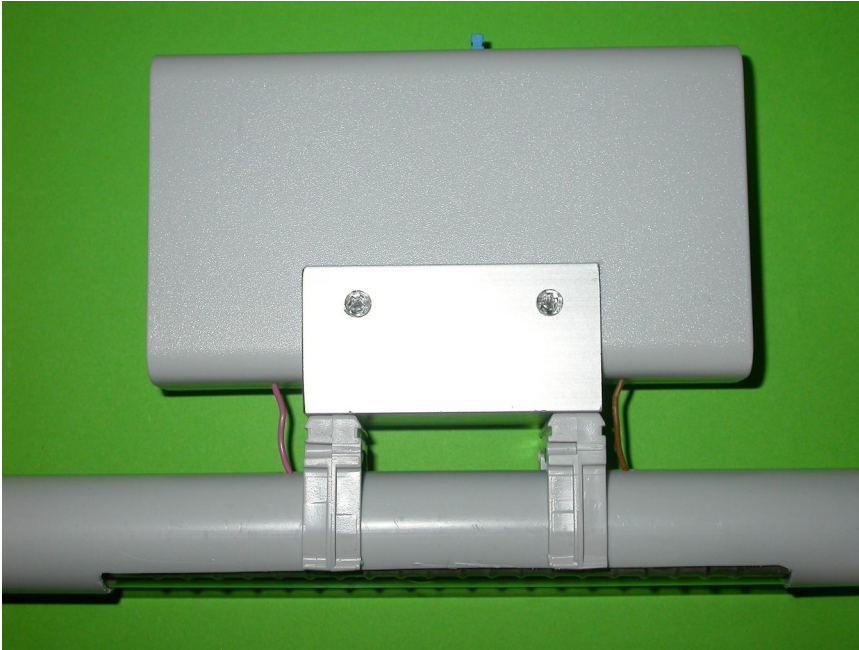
Bohrungen für Verbindungsdrähte und Montagewinkel
